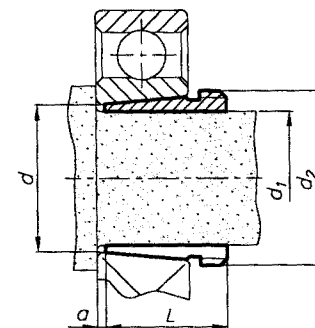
Закрепление внутреннего кольца подшипника на валу с использованием стяжной втулки
